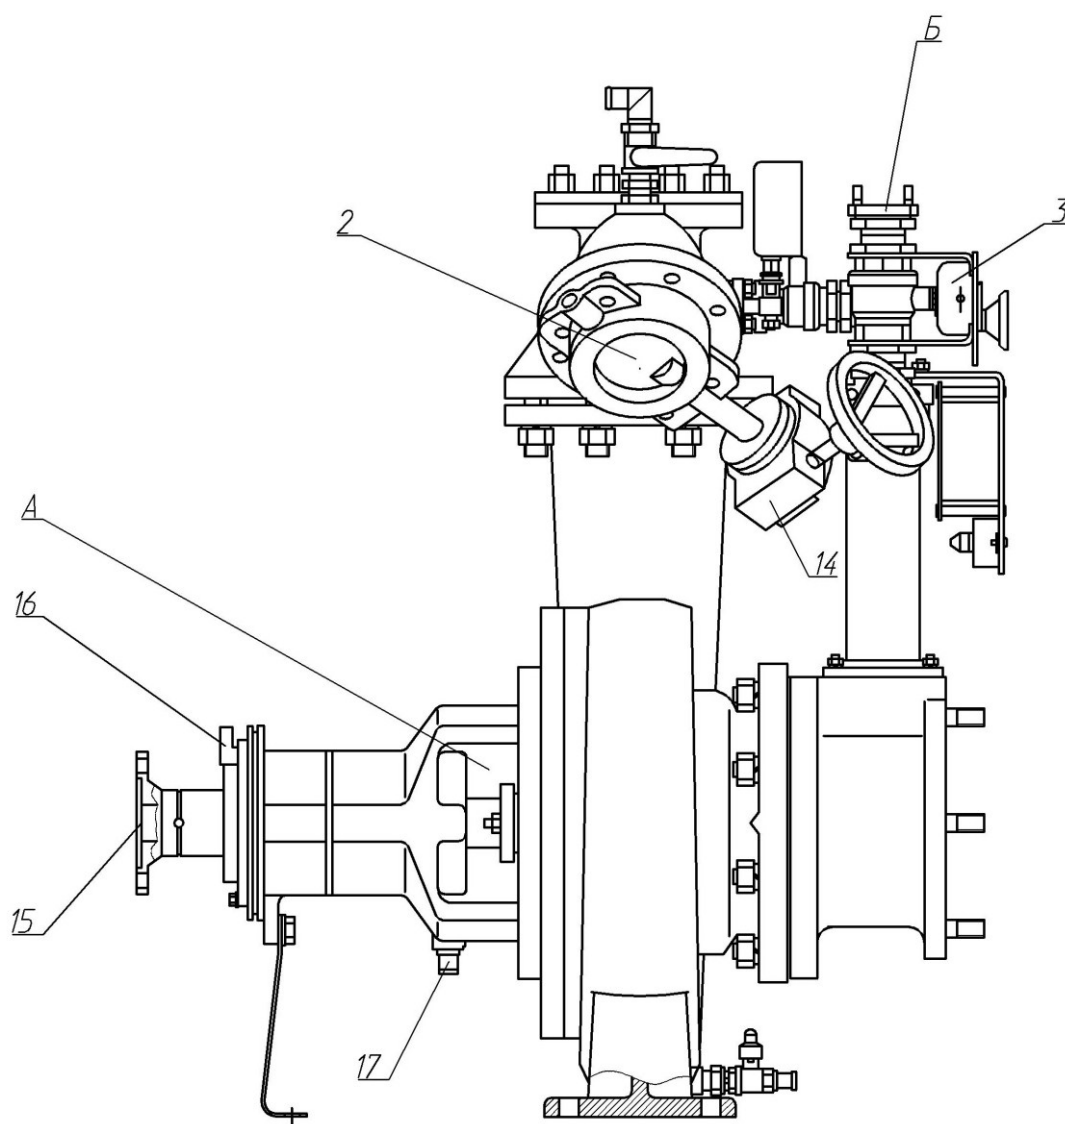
Насос НЦПН -100/100М: 2 – поворотная напорная задвижка; 3 – дозатор пеносмесителя; 14 – редуктор поворотной напорной задвижки; 15 – фланец привода; 16 – датчик тахометра; 17 – патрубок слива воды просочившейся через уплотнение вала рабочего колеса; А – окно для обслуживания уплотнения вала рабочего колеса; Б – штуцер для подачи пенообразователя.
